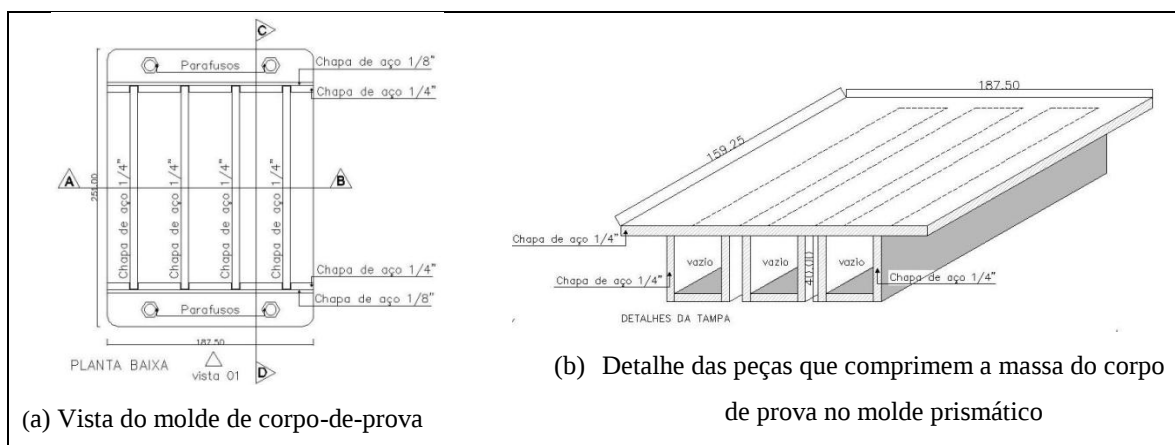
Detalhes do molde de corpo de prova prismático.
